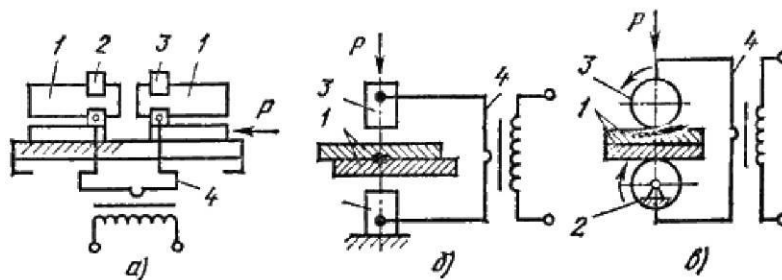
Схемы контактной сварки: а – стыковой; б – точечной; в – шовной
